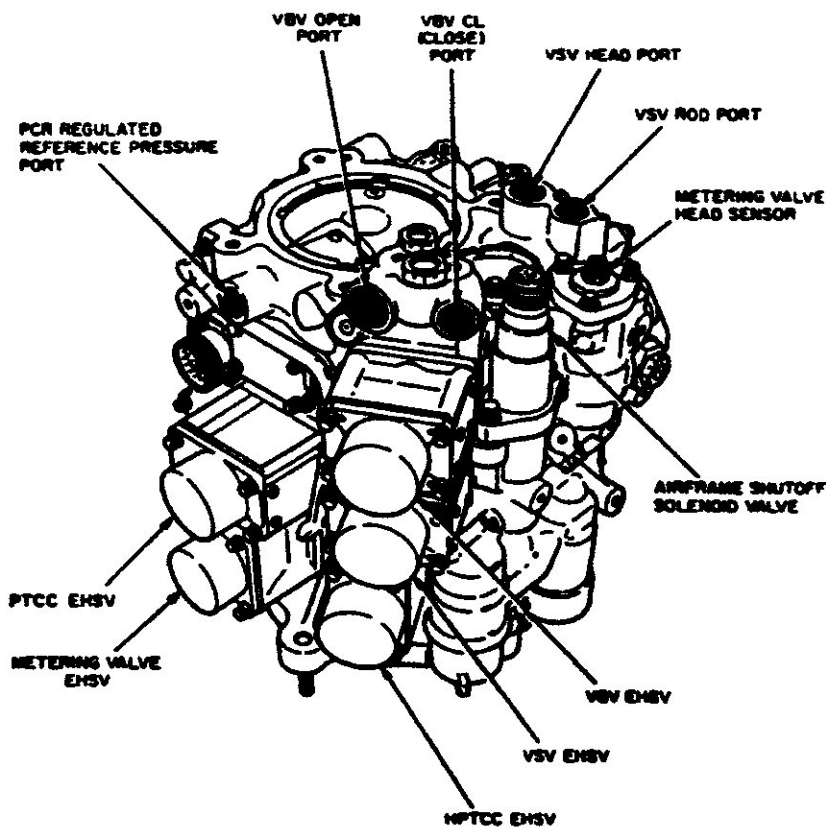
L'unité hydromécanique, ou le régulateur principal carburant
